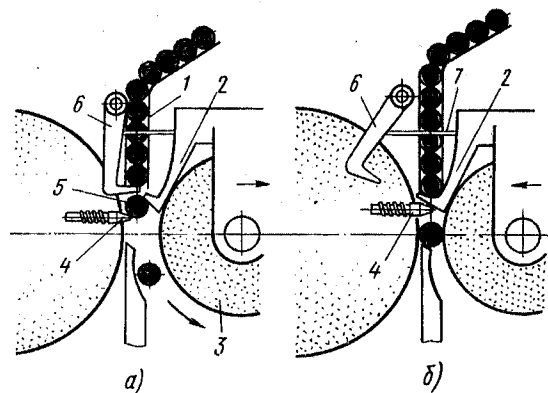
Устройство загрузки—разгрузки бесцентрово-шлифовального станка
